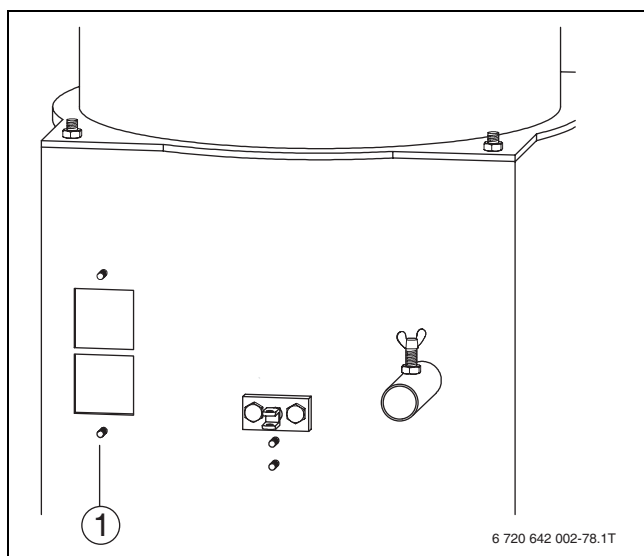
Kontrola snadného chodu motoru čištění hořáku
